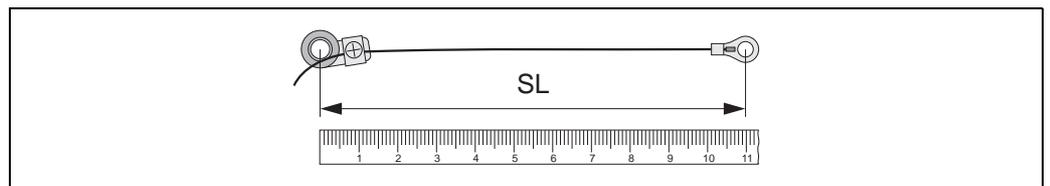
Fixierteil (a) und Kabelschuhe (b) mit einem Abstand entsprechend der Schnurlänge (SL)
